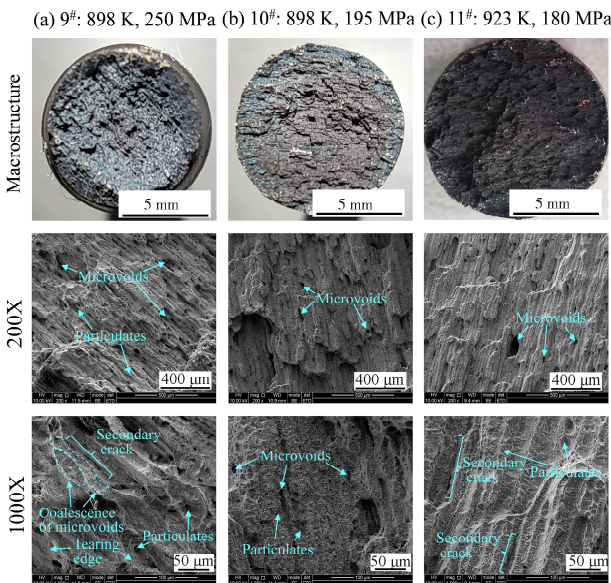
Co3W2/Co3W2 焊接接头断口形貌
